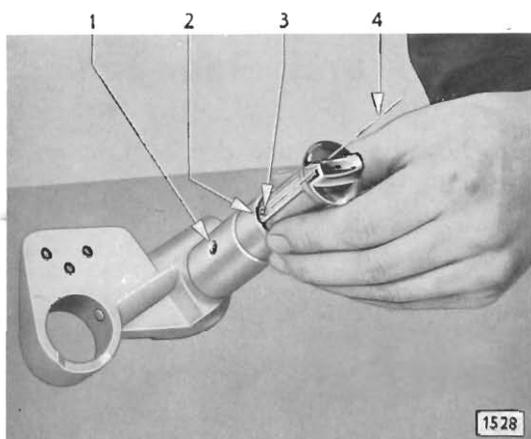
Schließzylinder in Lenk- und Zündschloß einbauen (am ausgebauten Schloß in Einbaulage dargestellt)
